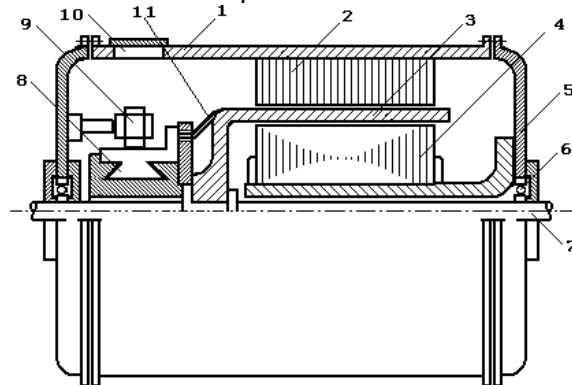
Servomotor cu rotor în formă de pahar.
